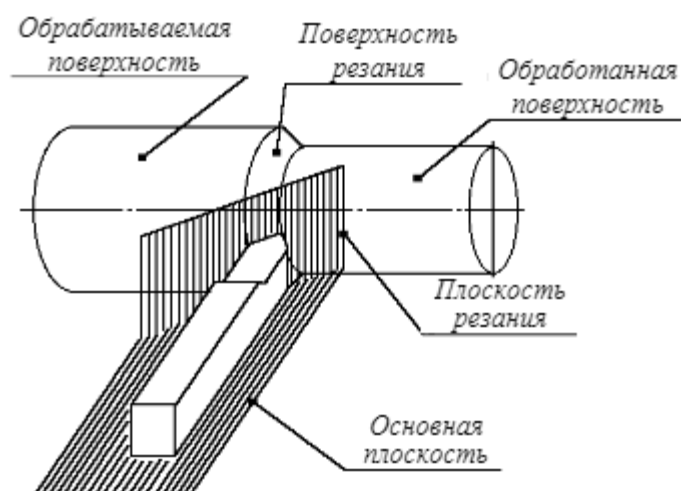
Координатные плоскости и поверхности заготовки при точении
